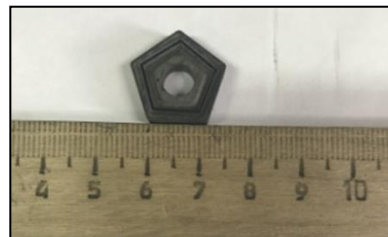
Внешний вид пластины из твердого сплава TI5K6
